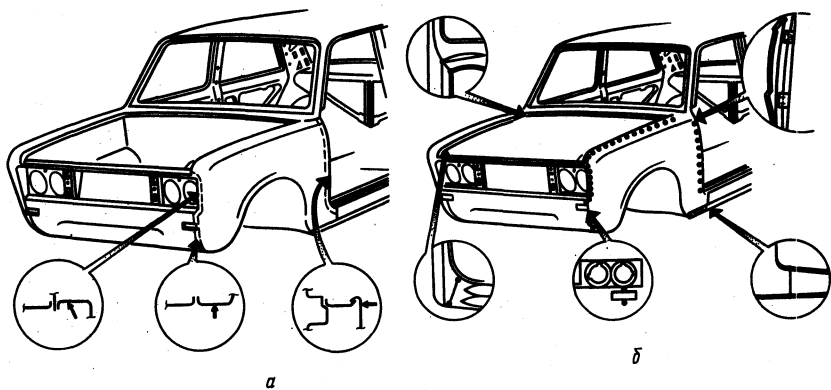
Замена переднего крыла автомобиля «Жигули»: а — место и линии рубки крыла; б — точки сварки крыла
